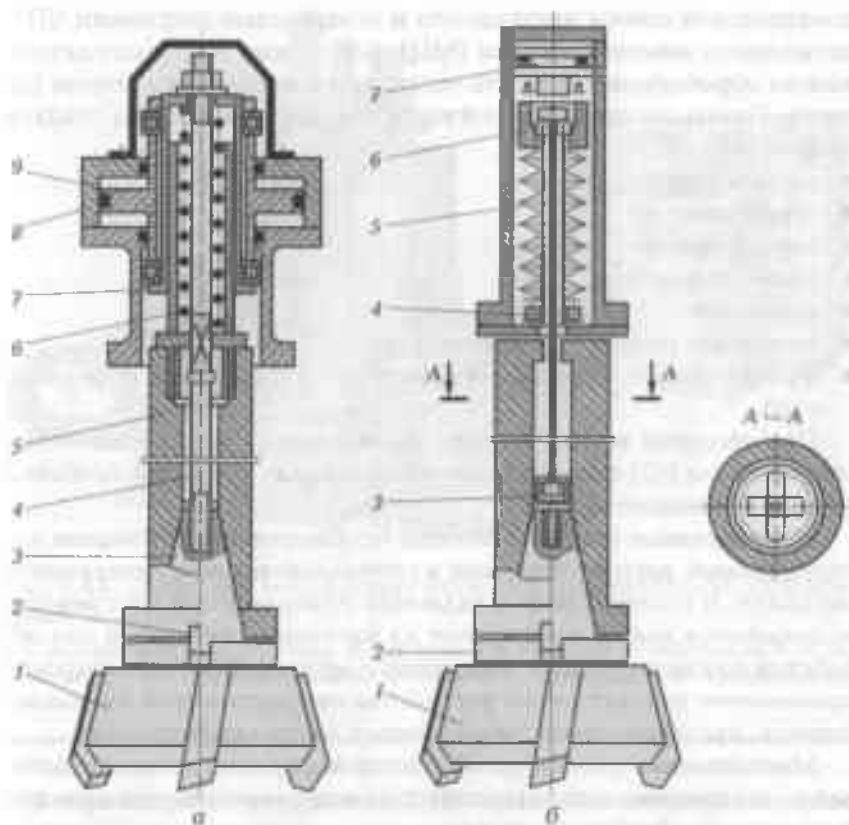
Приспособление для механизированного закрепления фрез в шпинделе:
